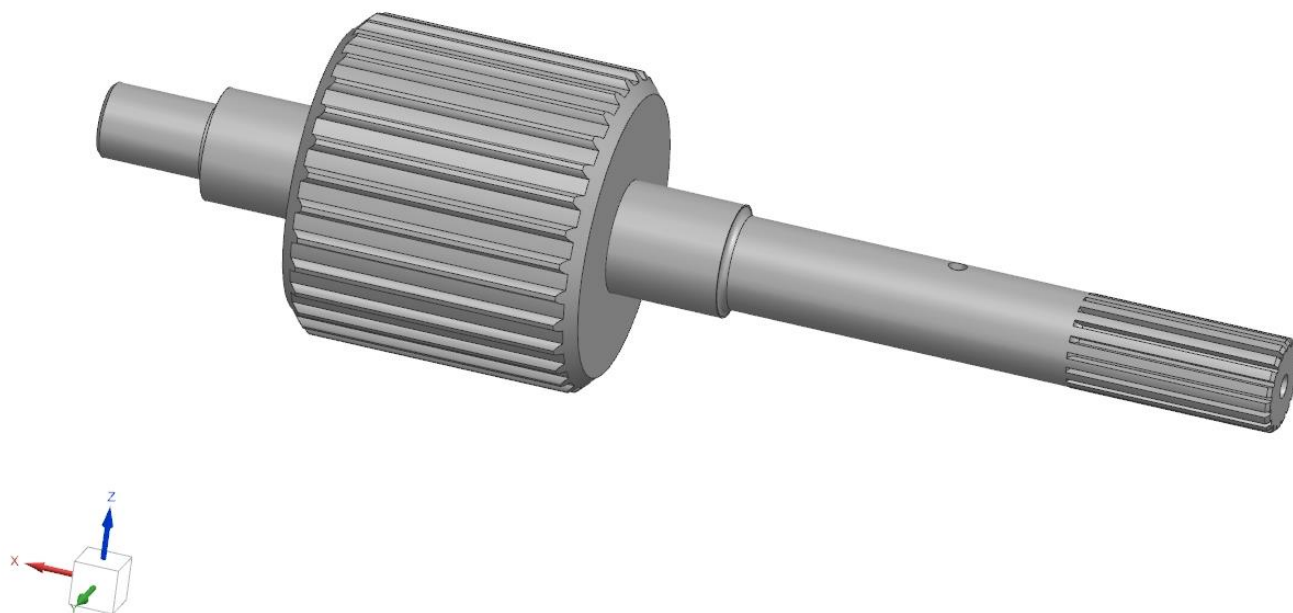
Створення 3д моделі деталі після обробки
